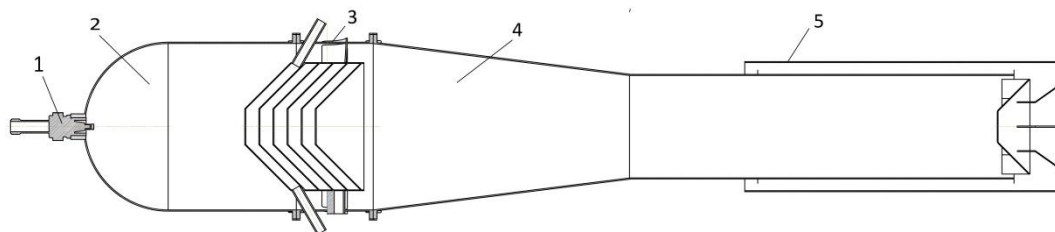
Конструкция двигателя: 1 - свеча зажигания; 2 - камера сгорания; 3 - газодинамический аппарат; 4 - вихревая камера - труба Ранка; 5 - эжектор с дросселем регулируемого сопла
